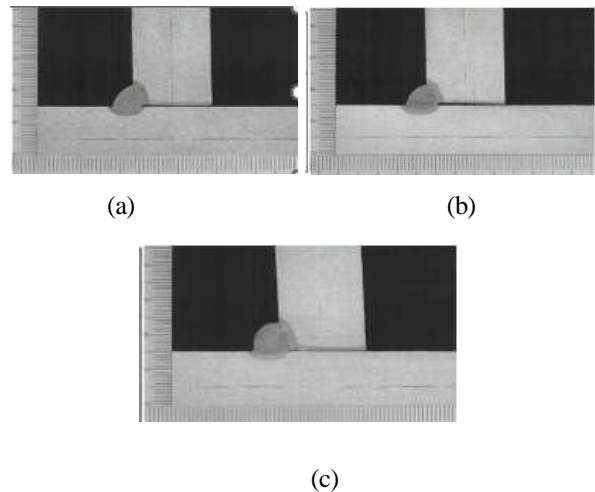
Pengukuran spesimen utama menggunakan *Welding gauge*. Hasil: (a) 6 mm, (b) 7mm, (c) 8mm
